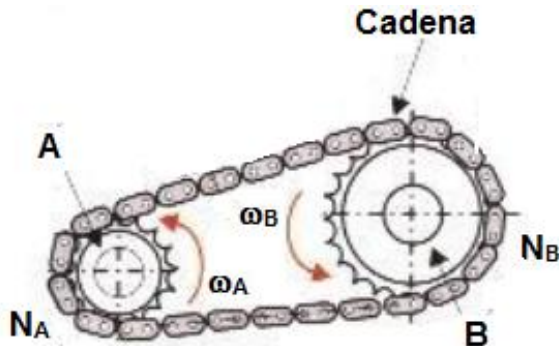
Transmisión con Sprockets y cadena de rodillos
